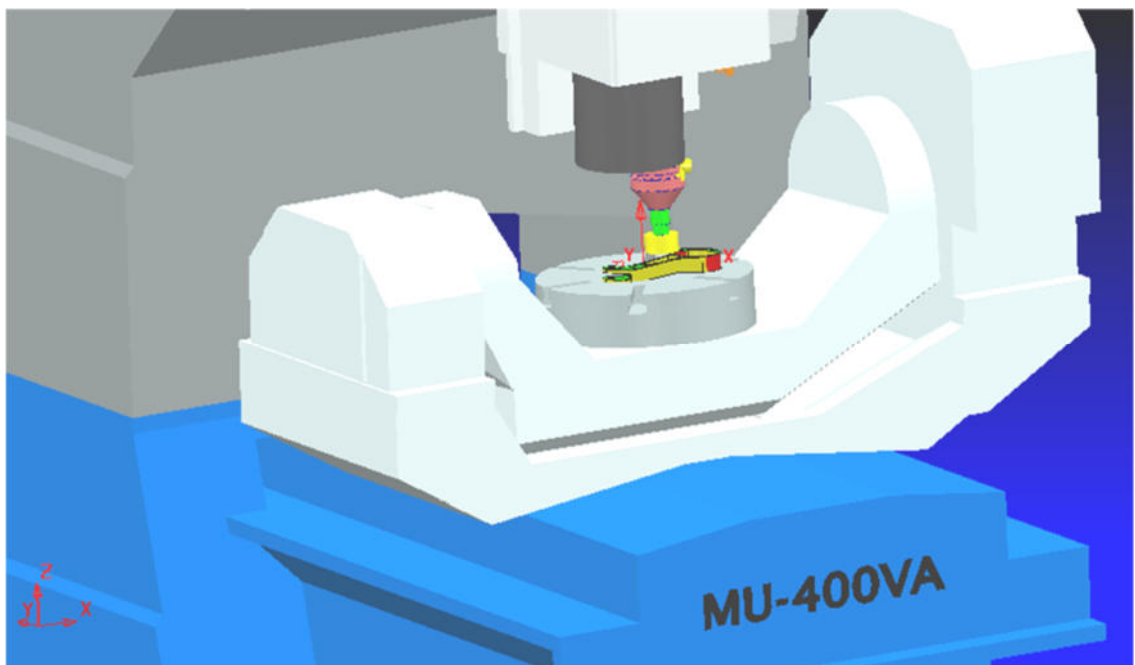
Загальний вигляд деталі «Ланка» на верстаті з ЧПК
